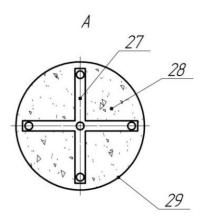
Форма сечения резервуара вибростанка согласно схеме рис. 1
